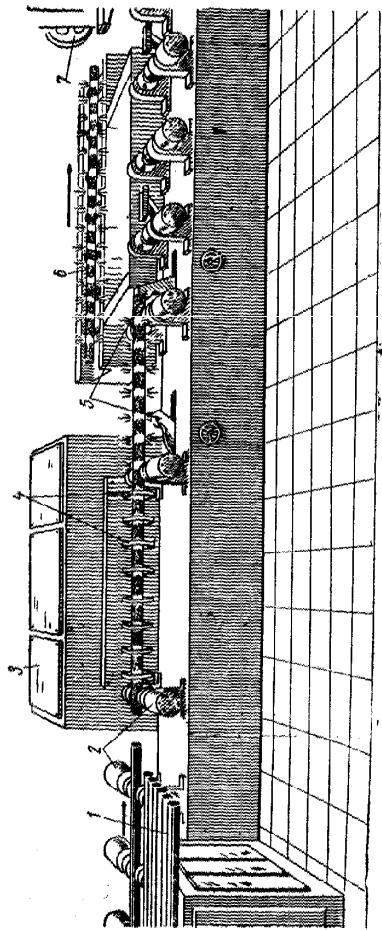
Устройство для нагрева заготовок под резку на ножницах:
